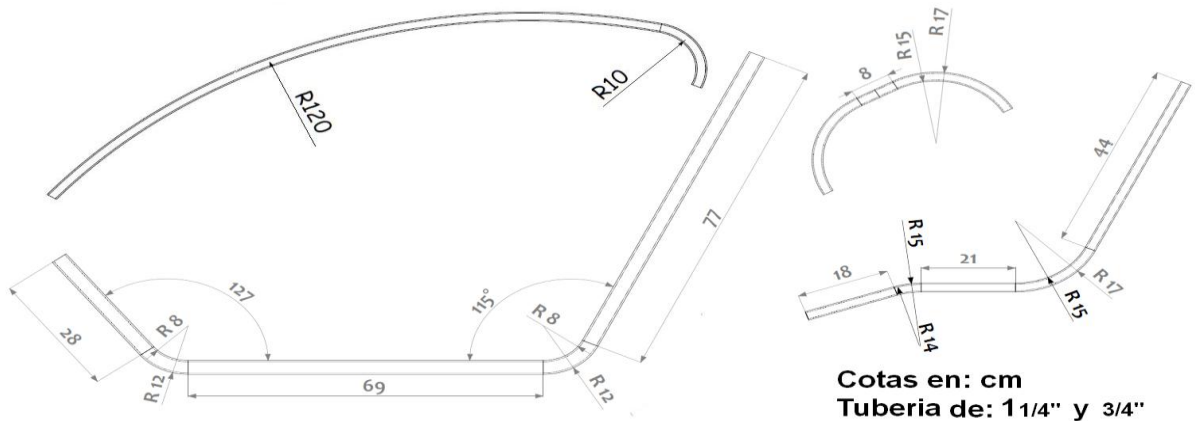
Imagen de los planos del vehículo. La sección principal del chasis es de 1 1/4", los perfiles de la silla y la barra antivuelco son en tubería de 3/4". Fuente: Franklin Patiño.
